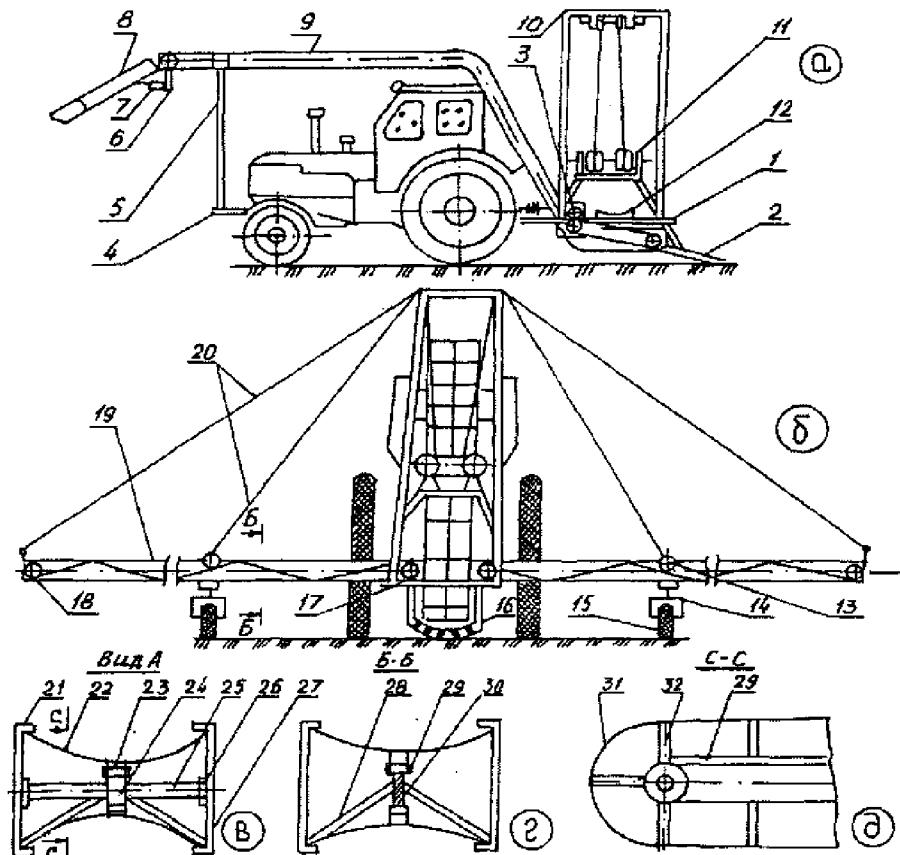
Агрегат для выборочной уборки плодов: 1 – опорная рама; 2 – лоток; 3 – редуктор; 4 – балка; 5,10 – стойка; 6 – упор; 7 – гидроцилиндр; 8 – укладчик; 9 – погрузочный транспортер; 11 – лебедка; 12 – транспортеры боковые; 13 – шарнир; 14 – опорная стойка; 15 – опорное колесо; 16 – эластичный материал; 17 – шарнирно-поворотное крепление; 18 – натяжные звездочки; 19 – ферма; 21 – боковины; 22 – лотковый транспортер; 23 – приводная цепь; 24 – натяжное устройство; 25 – вал; 26 – подшипники; 27 – несущая ферма; 28 – распорки; 29 – направляющая дорожка; 30 – средняя часть фермы; 31 – эластичный материал; 32 – металлические дуги
